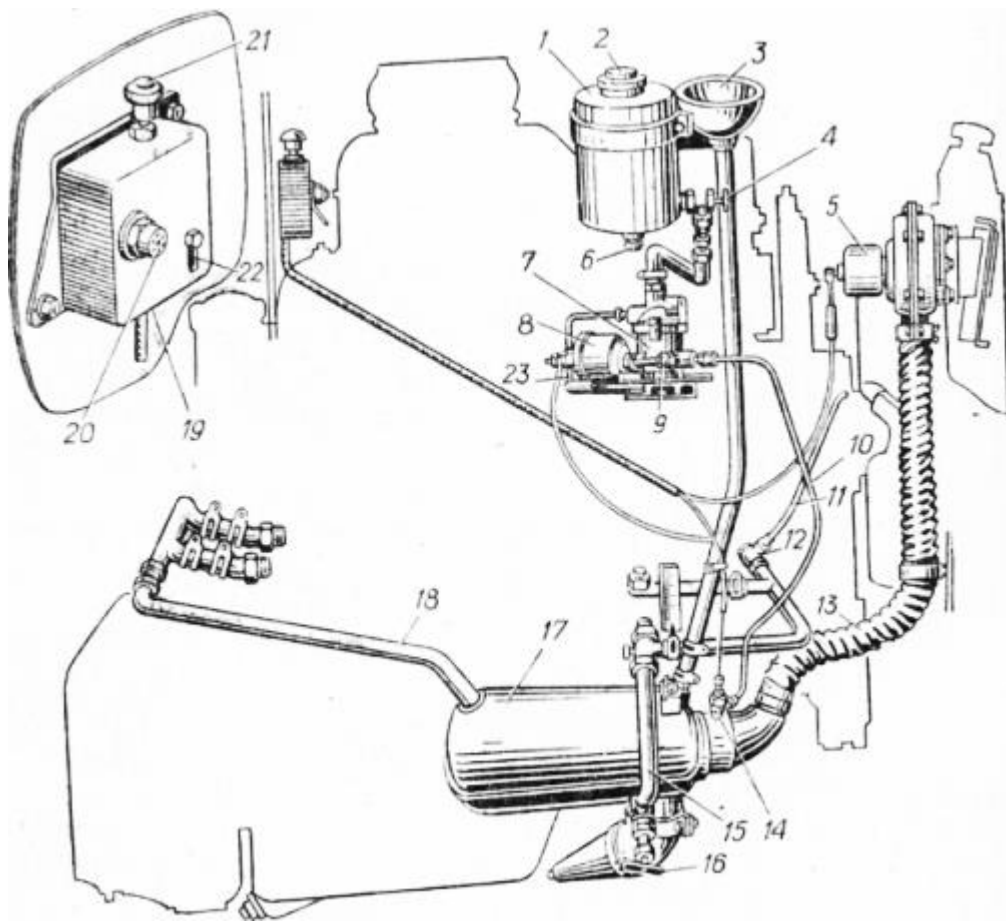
Пусковой подогреватель двигателя ЗИЛ-130: 1— топливный бачок; 2 — пробка бачка; 3 — наливная воронка; 4— кран; 5 — электродвигатель с вентилятором; 6 — пробка сливного отверстия; 7 — регулятор подачи топлива; 8 — электромагнитный клапан; 9 — регулировочная игла; 10 — трубка от регулятора к камере сгорания котла; 11 — ручка управления краном; 12 — сливной кран трубопровода подогревателя; 13 — шланг подвода воздуха; 14 — свеча накаливания; 15 — отводящая трубка от двигателя к котлу; 16 — сливной кран котла; 17 — котел подогревателя; 18 — подводящая трубка от котла к двигателям; 19 — пульт управления; 20 — контрольная спираль; 21 — переключатель; 22 — выключатель свечи; 23 — трубка слива топлива
